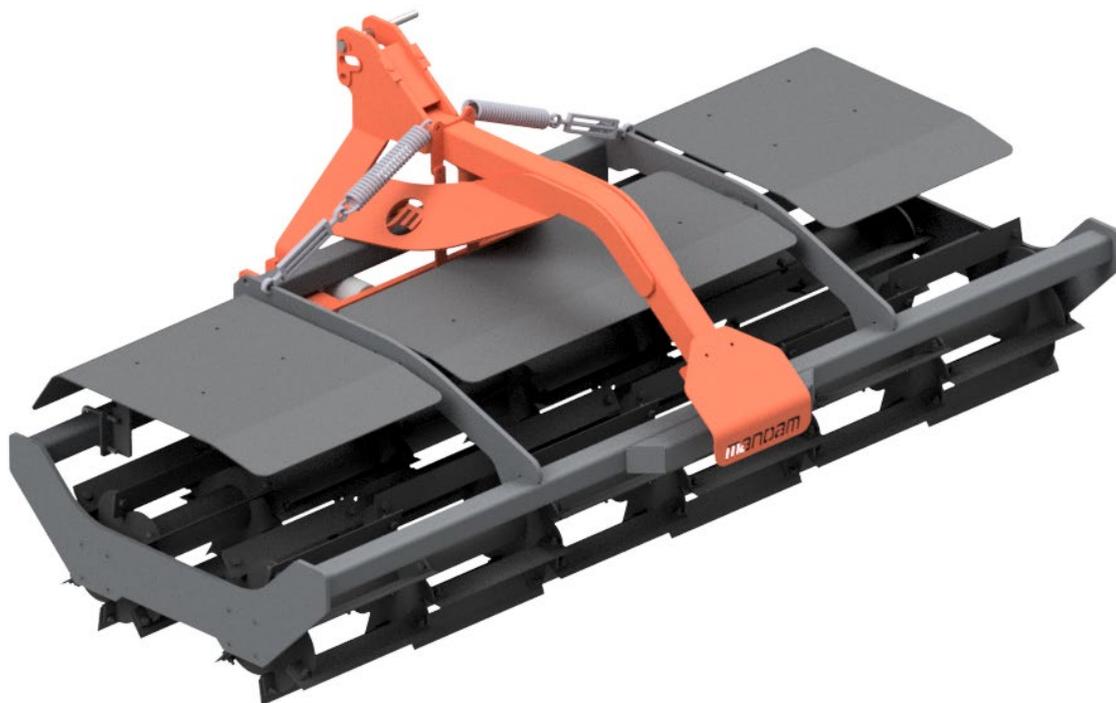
Rouleau à couteaux Tandem 3,0 avec protections supérieures.
